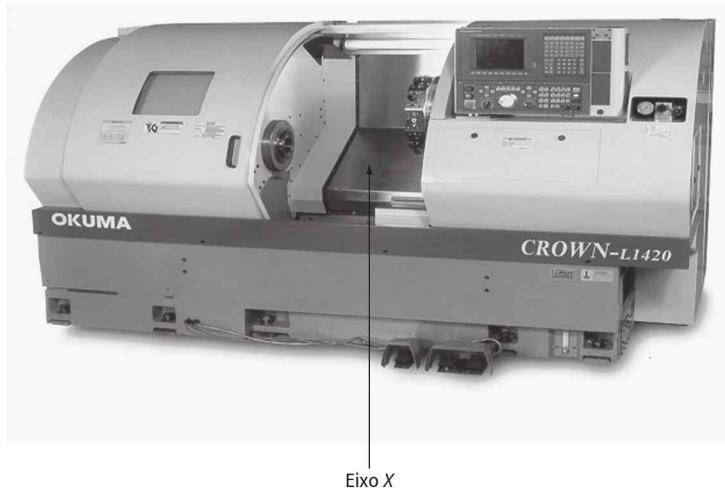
O eixo X de um torno com barramento inclinado é rotacionado em relação ao solo para melhorar a refrigeração e a remoção de cavaco e para auxiliar o acesso do operador durante a preparação.
